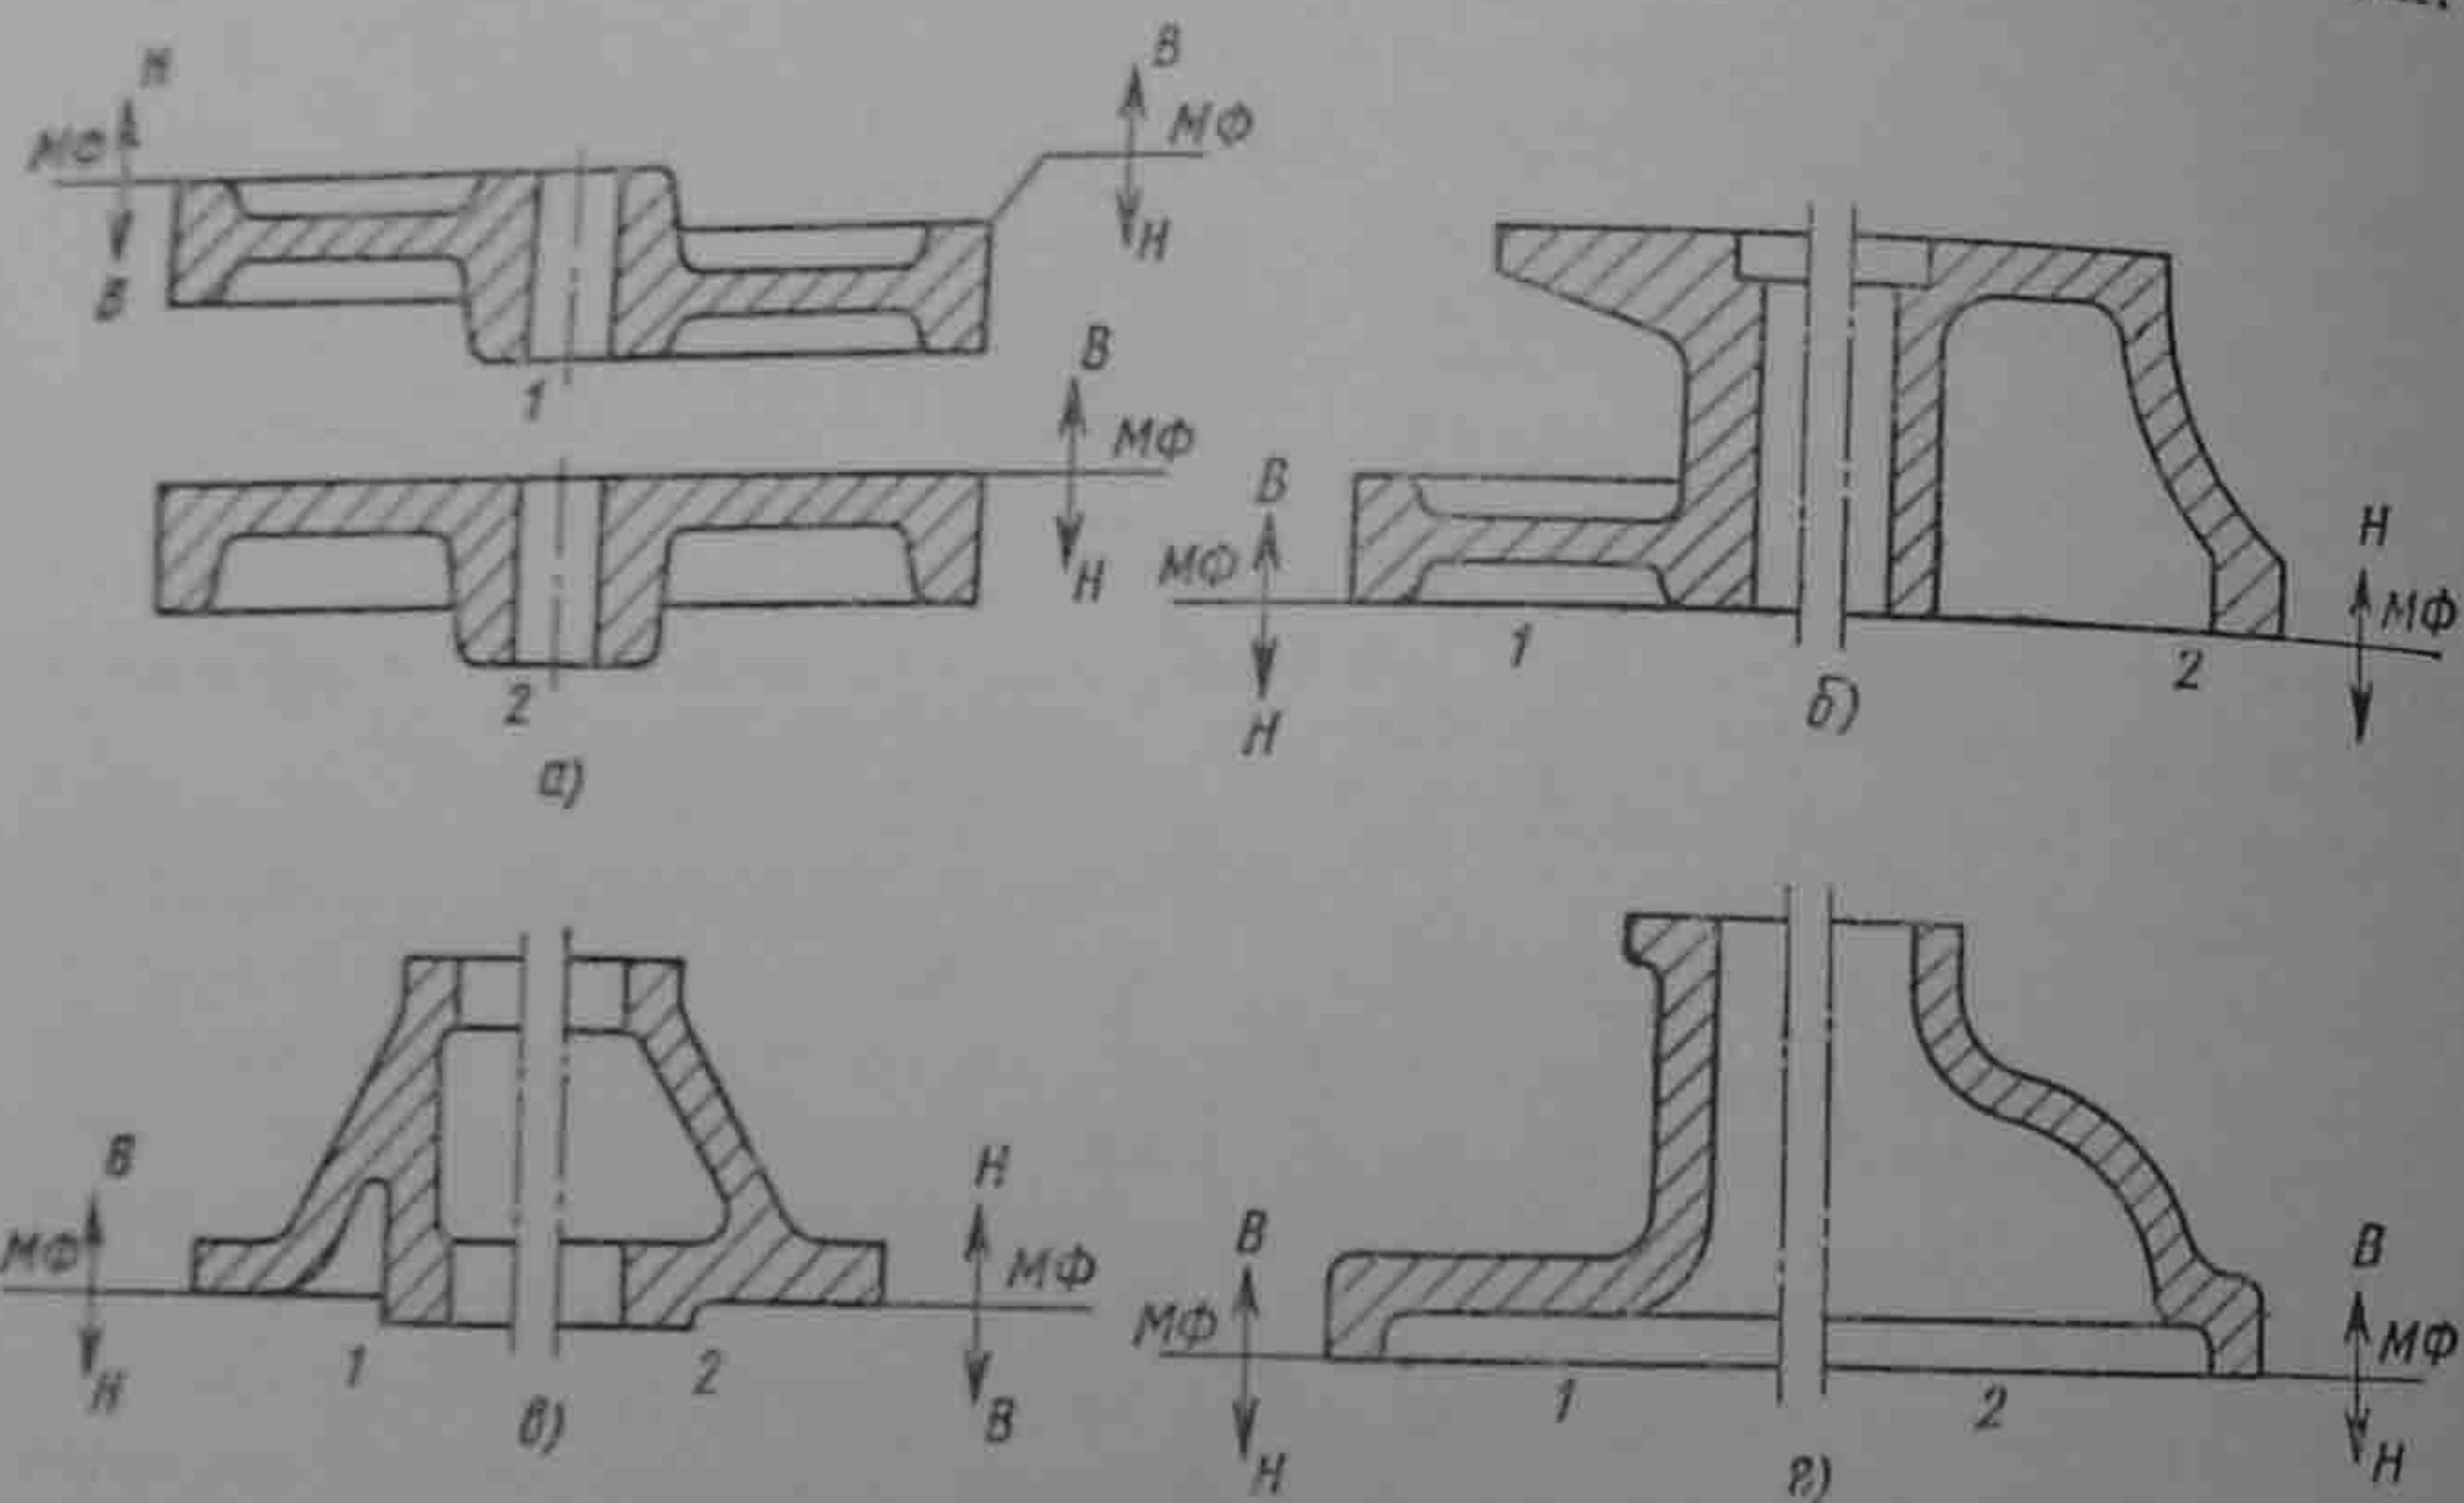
Изменение конструкции детали для облегчения формовки и изготовления моделей:
